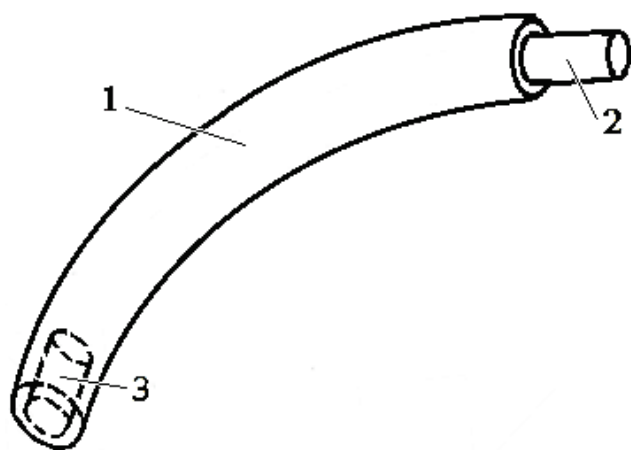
Соединительный элемент сегментов спиралевидной крепи: 1 — корпус соединительного элемента; 2 — вставной выступ; 3 — выемка
